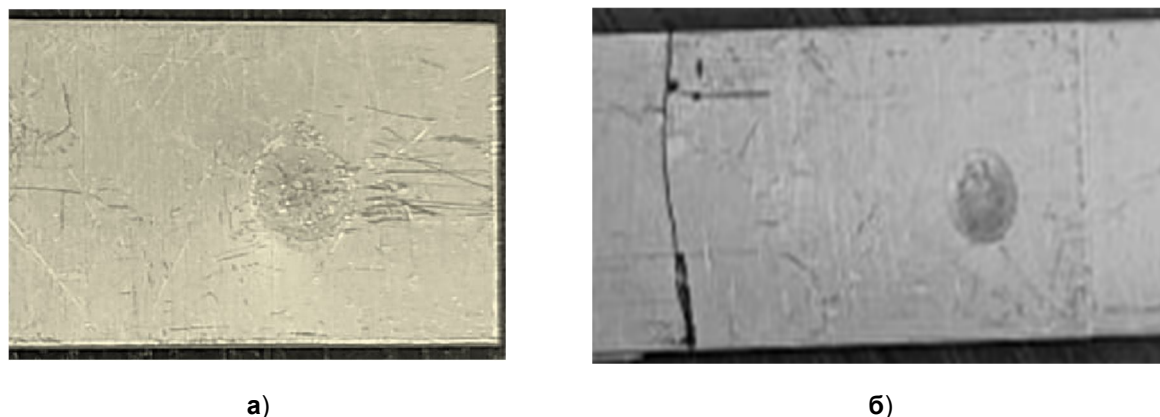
Виды разрушения сварных образцов при испытании на вибрационную прочность: а – разрушение по сварной точке, б – разрушение по основному металлу
